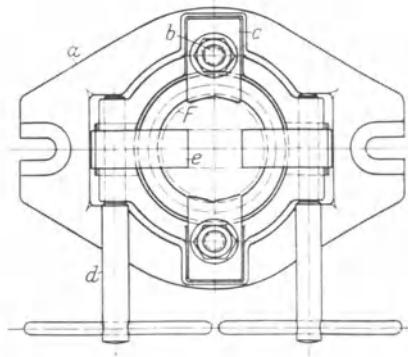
Fräsvorrichtung zum Fräsen der Backenführungen im Spannfutter.
